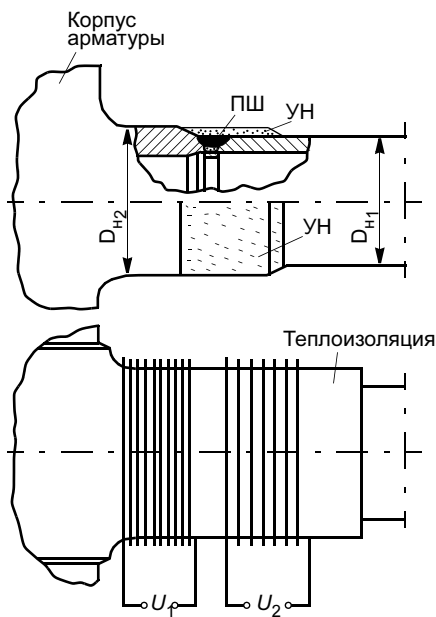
Рекомендуемая схема сварочной технологии ремонта стыкового сварного соединения разнотолщинных трубных элементов $\varnothing 290 \times 50$ мм/ $\varnothing 273 \times 32$ мм (сталь соответственно 15Х1М1ФЛ/12Х1МФ, металл шва 09Х1МФ): а, б — см. рис. 7
